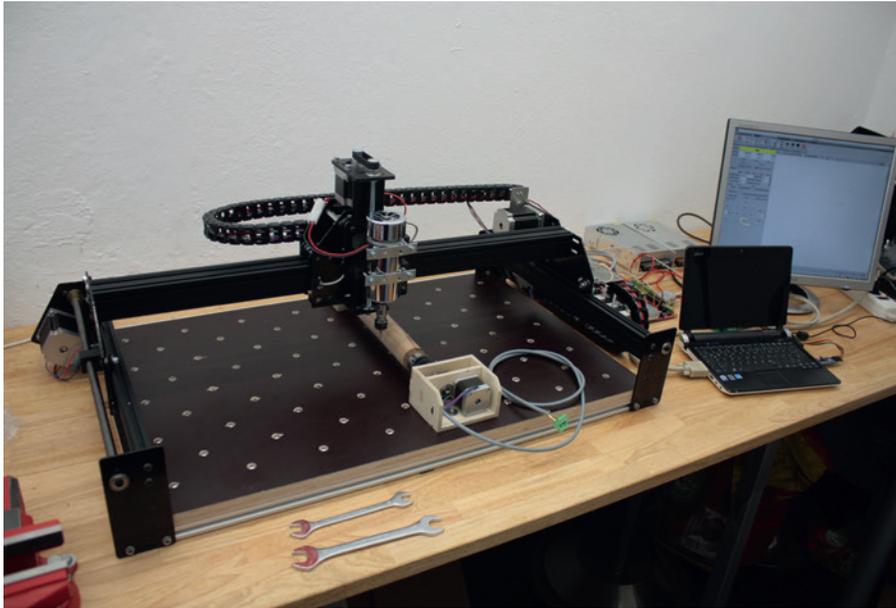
Größeres Kaliber: die Shapeoko-T mit Spindeltrieben, MaXYposi-Steuerung und vierter Achse
